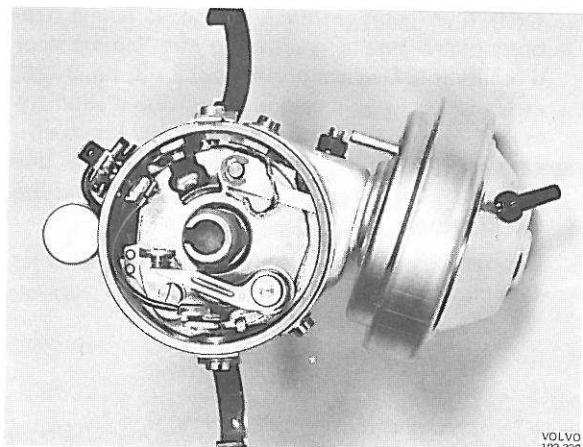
Evidement pour réglage de contacts de rupteur
